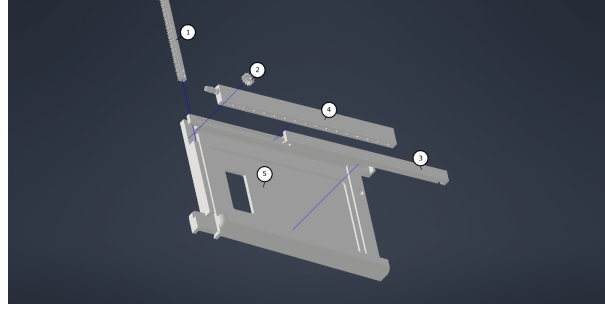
Vista explodida da montagem do mecanismo de translação do ASCM: (1) Cremalheira (*Gear-Rack*); (2) Pinhão (*Gear*); (3) Suporte do Rodo (*Wiper Support*); (4) Suporte de Aspersão (*Sprinkler*); (5) Suporte dos Painéis (*Panel Support*). Fonte: Elaborado pelos autores.
